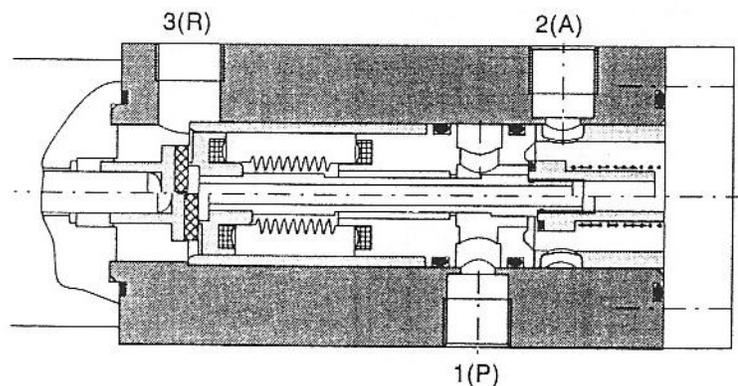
Vista seccionado de un regulador de presión con ajuste mecánico
